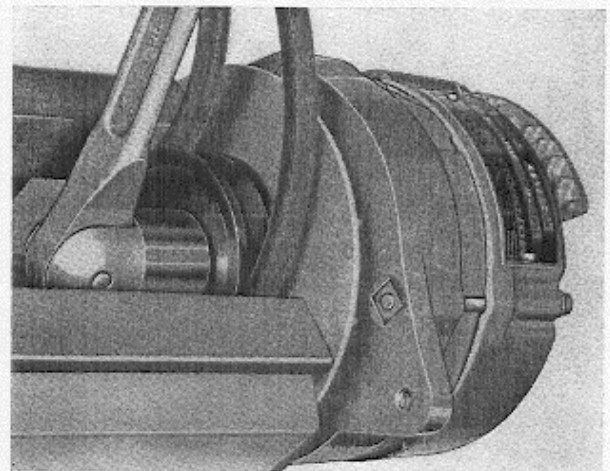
Ausbau der Mutter für die Riemenscheibe
